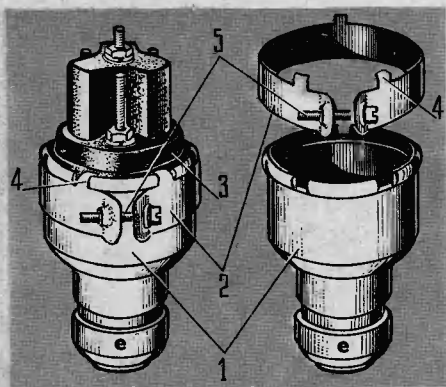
Разборный замок зажигания: 1 — корпус; 2 — стяжной хомут; 3 — эбонитовая панель; 4 — отогнутый зубец хомута; 5 — стяжной болт.
